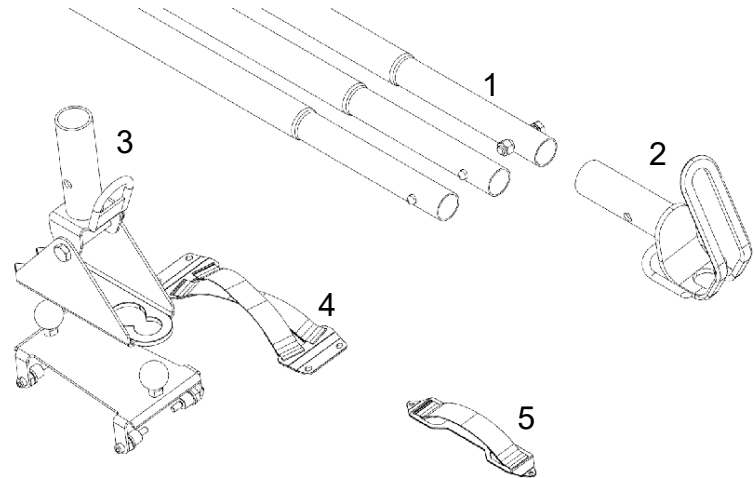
Komponenten der Raupeneinsatzwerkzeuge.
